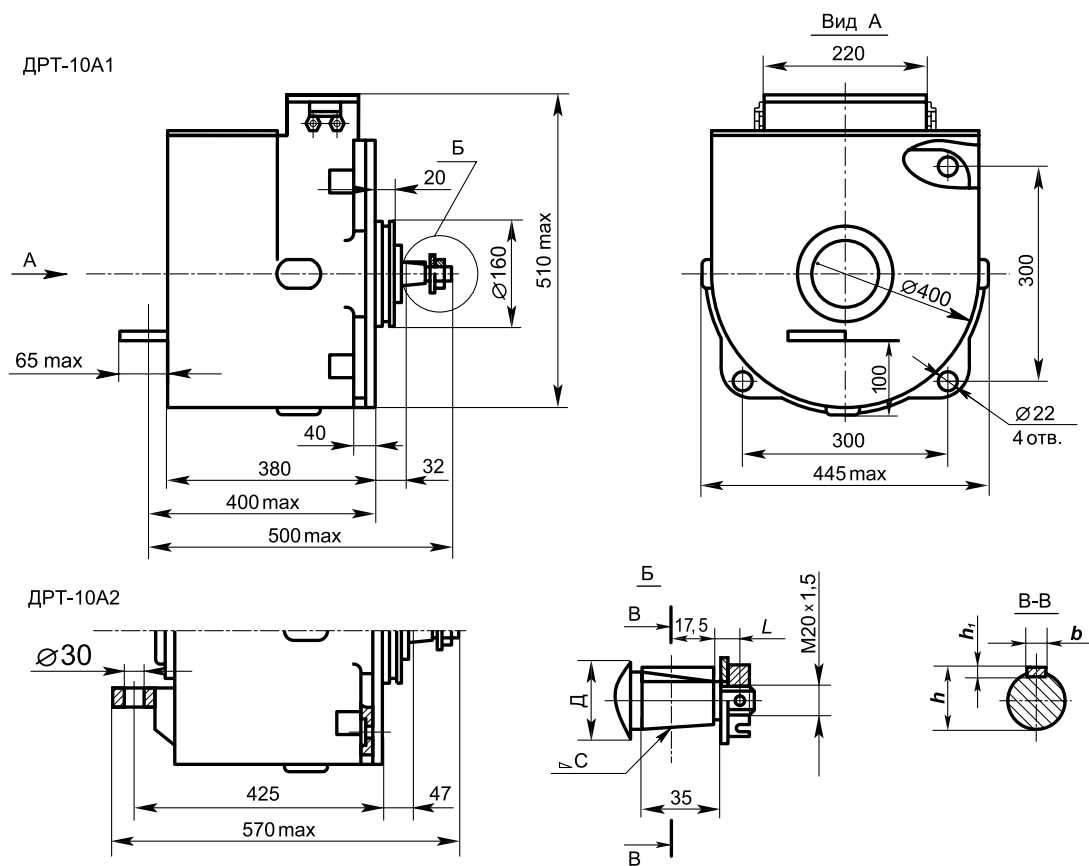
Габаритные и установочные размеры электродвигателей ДРТ-10А1, ДРТ-10А2
